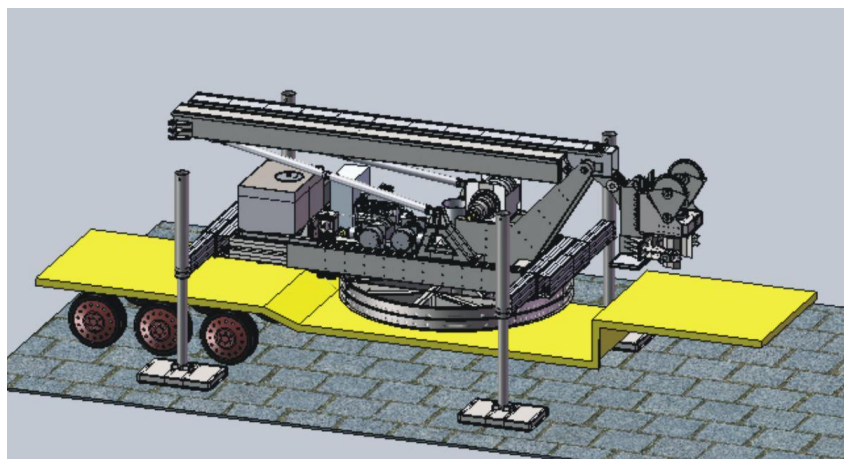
Perfuratriz apoiada no solo e com a prancha de carregamento posicionada sob sua estrutura.
